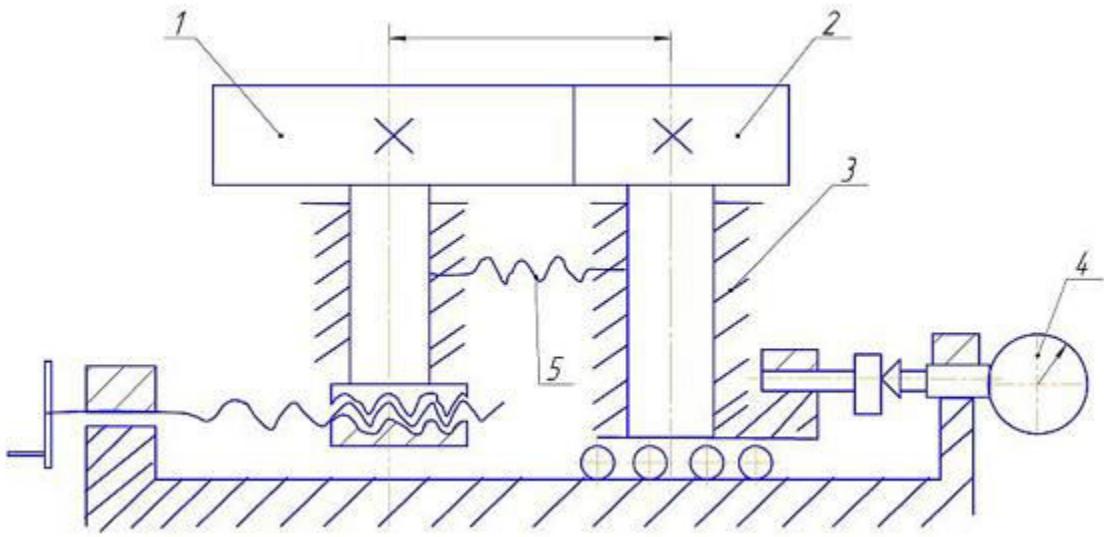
Схема межцентромера: 1 – контролируемое зубчатое колесо; 2 – измерительное зубчатое колесо; 3 – плавающая каретка; 4 – измерительная головка (индикатора); 5 – пружина.
